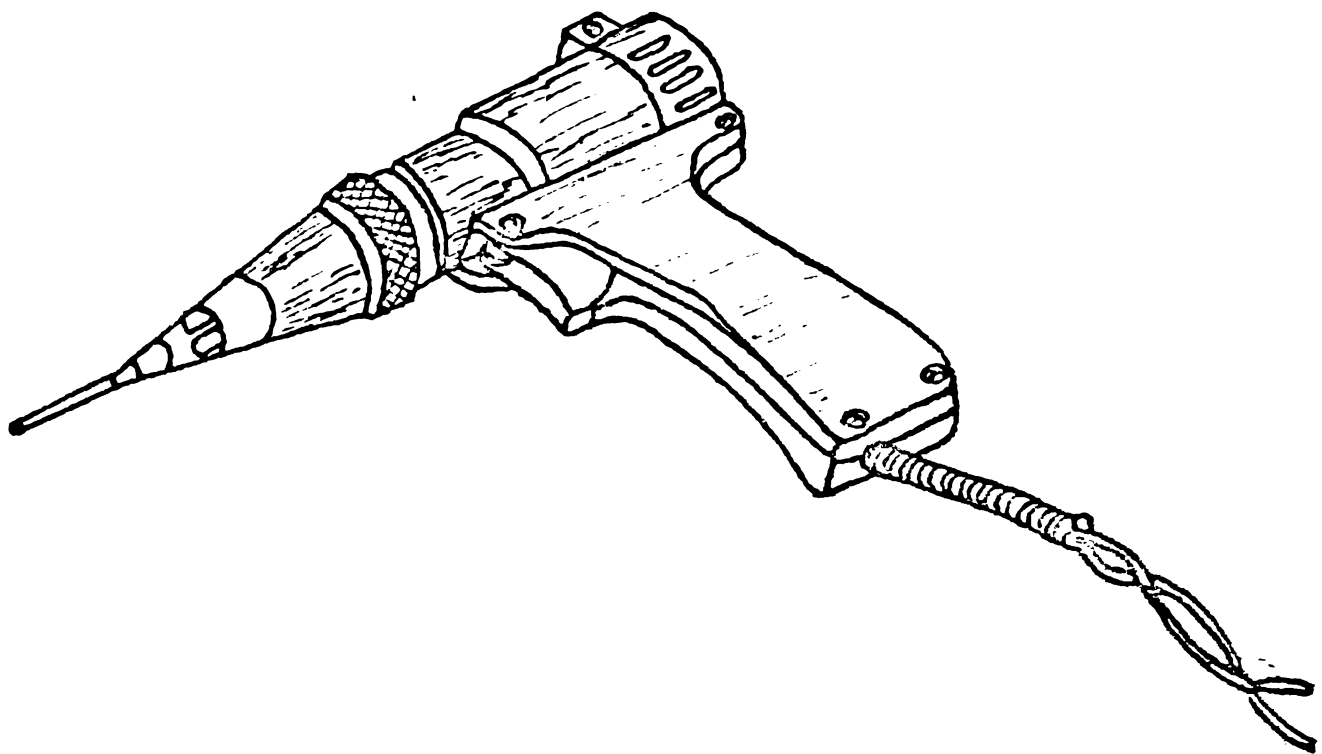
Приспособление для накрутки НП-48 с насадкой для провода МНВ-0,05
